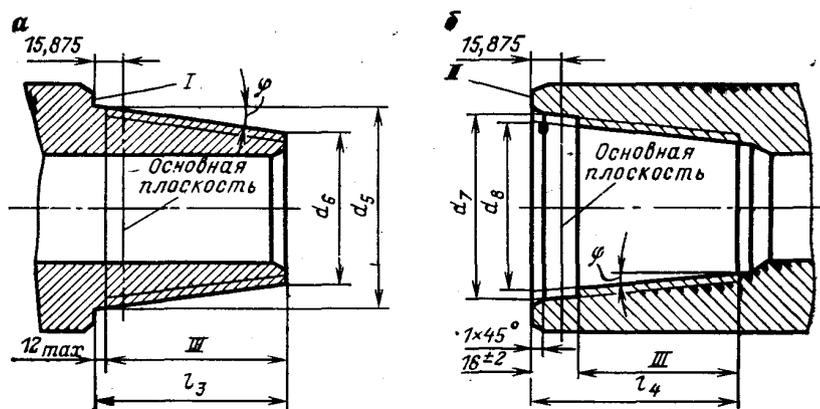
Ниппель (а) и муфта (б) замка с замковой резьбой:
